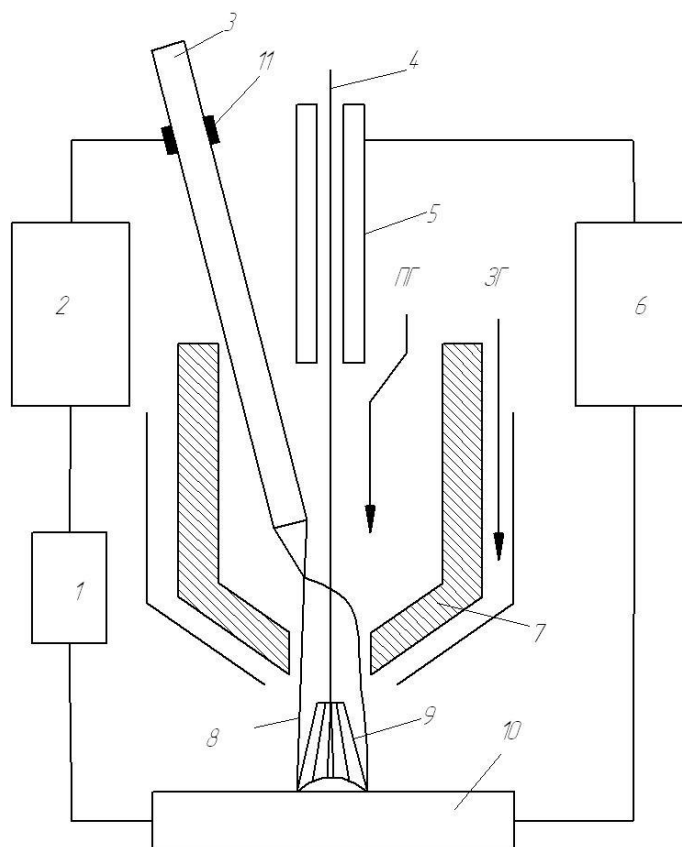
Схема плазменной сварки-наплавки плавящимся электродом
